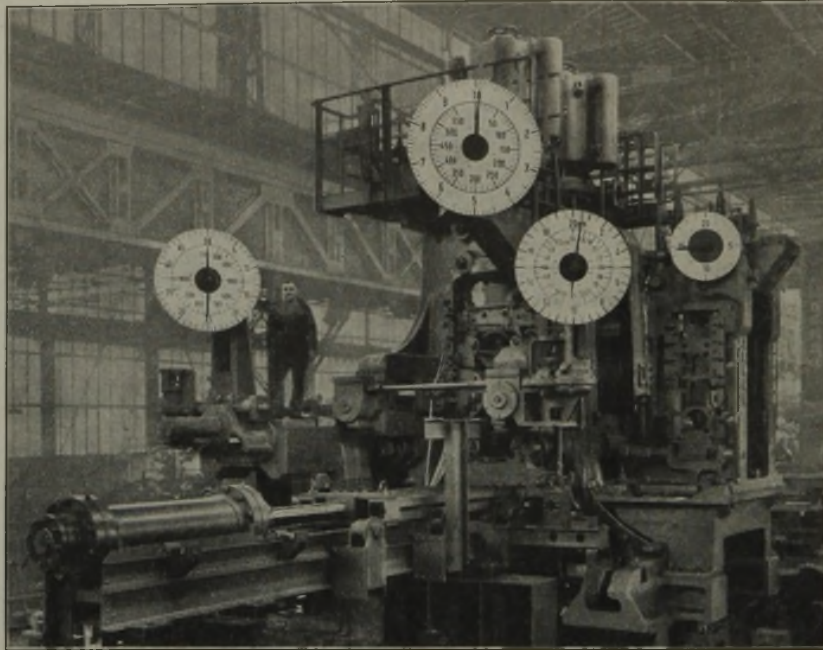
Streifenstauengerüst (links), Hauptgerüst (Mitte) und Flanschenstauengerüst (rechts).
